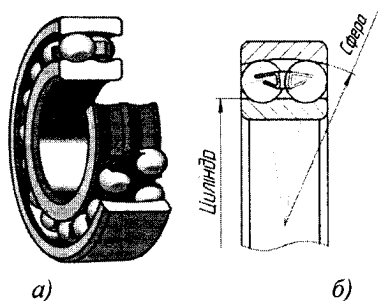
Кульковий радіальний дворядний сферичний підшипник
